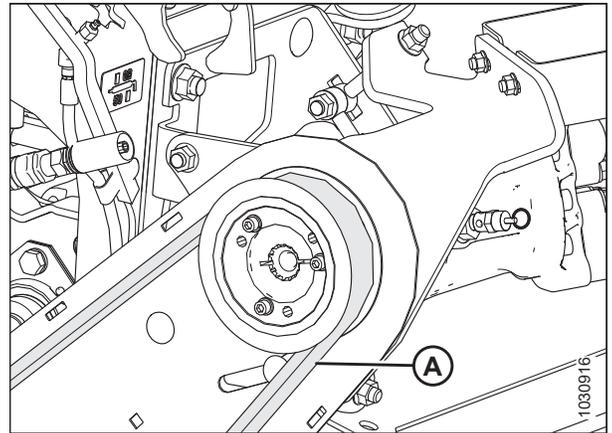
Ведущий шкив — Гидромотор привода плющилки
